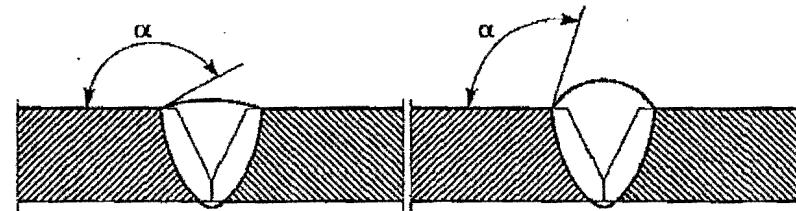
44. Неправильный профиль сварного шва
